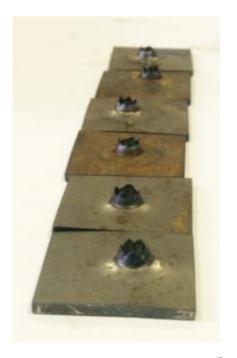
Тонколистовые заготовки с образованными в них отверстиями
